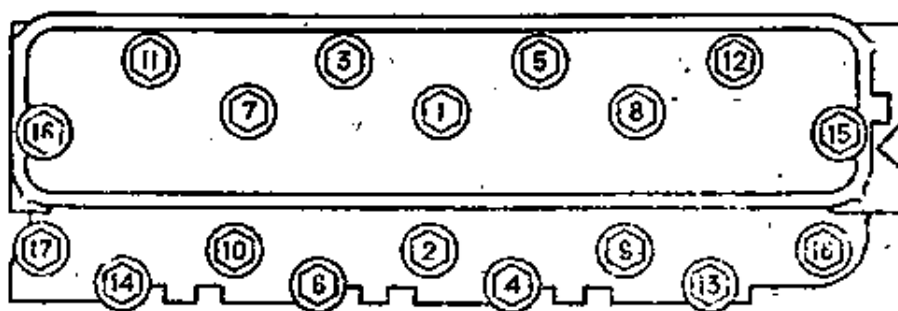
Порядок затяжки винтов ГБЦ двигателя ЗМЗ-53
